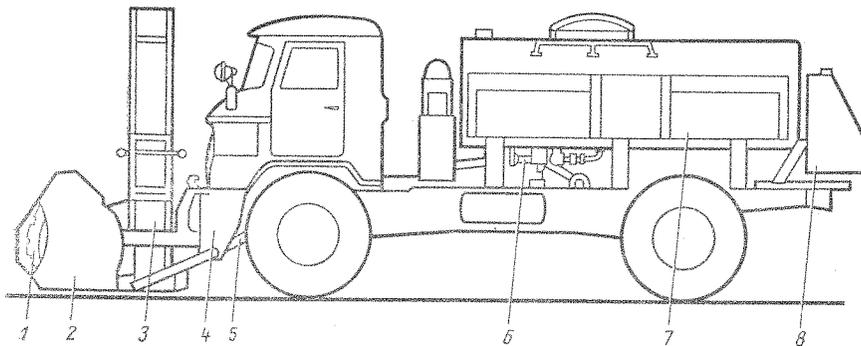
Общий вид фрезерно-роторного снегоочистителя РС-66 с поливомосным оборудованием
